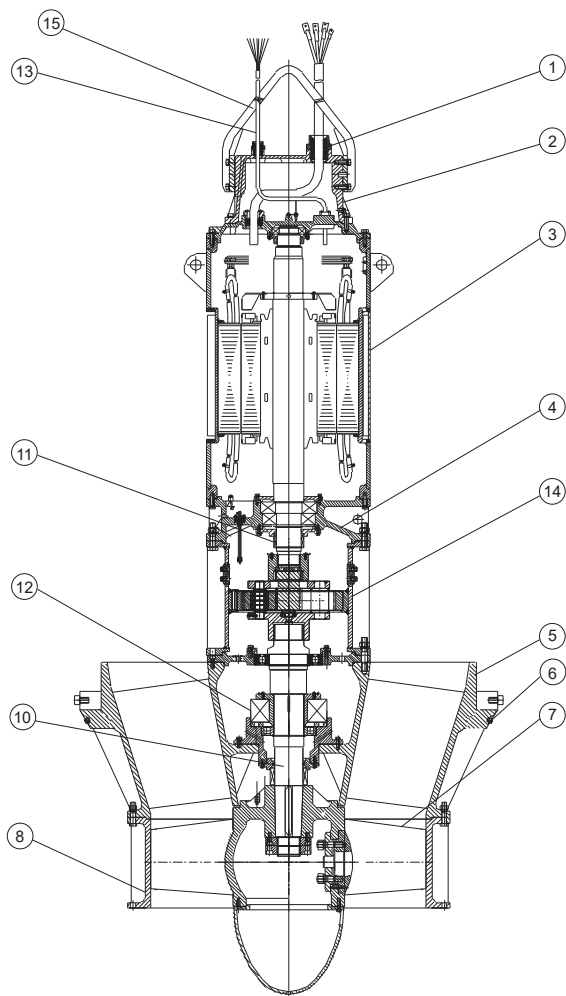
Чертеж разреза насоса ZQX с планетарным редуктором
